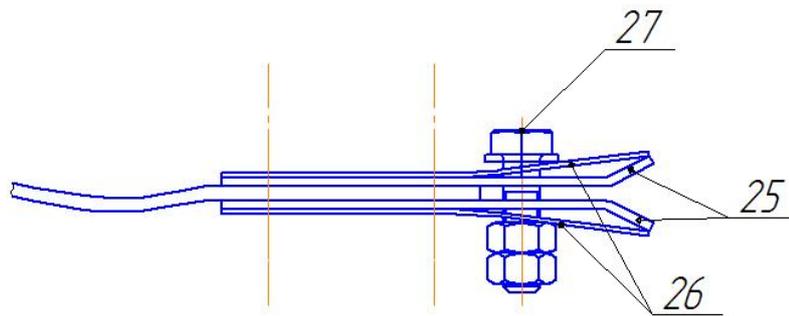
Соединение и установка валов привода 6, 7, 8
